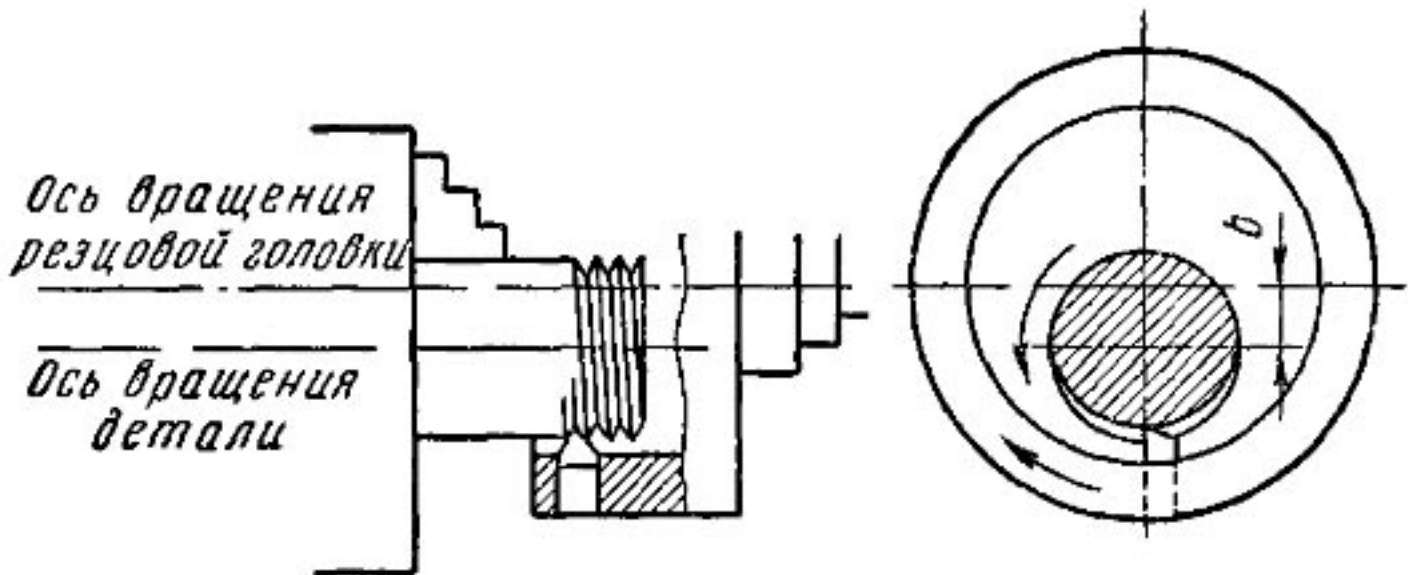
Схема нарезания наружной резьбы вращающейся резцовой головкой
